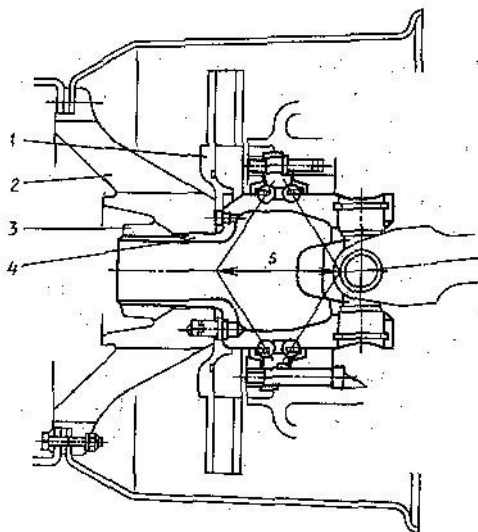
Двухрядный радиально-упорный шарикоподшипник четвертого поколения фирмы СНР, применяемый на задних ведущих колесах гоночного автомобиля формулы 1 фирмы «Рено». В наружное кольцо привернутое к опоре подшипника колеса, с обеих сторон вставлены уплотнительные манжеты, двойные кромки которых работают, как и шарики, по специально выполненному внутреннему кольцу. Последнее воспринимает с одной стороны крестовину шарнирного вала, а с другой — тормозной диск и колесо, центрирует обе эти детали и благодаря резьбе на трубчатом конце дает возможность быстрой смены колеса. Слева видна гайка необходимого для этого быстродействующего зажима
